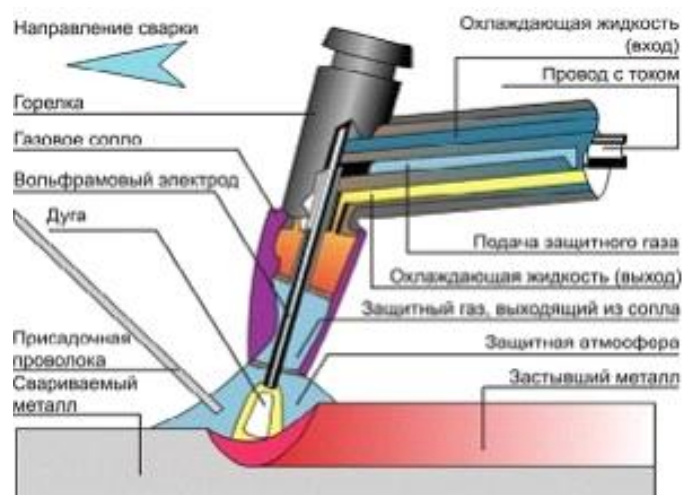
Сварка неплавящимся электродом в среде защитного газа с применением полуавтомата
